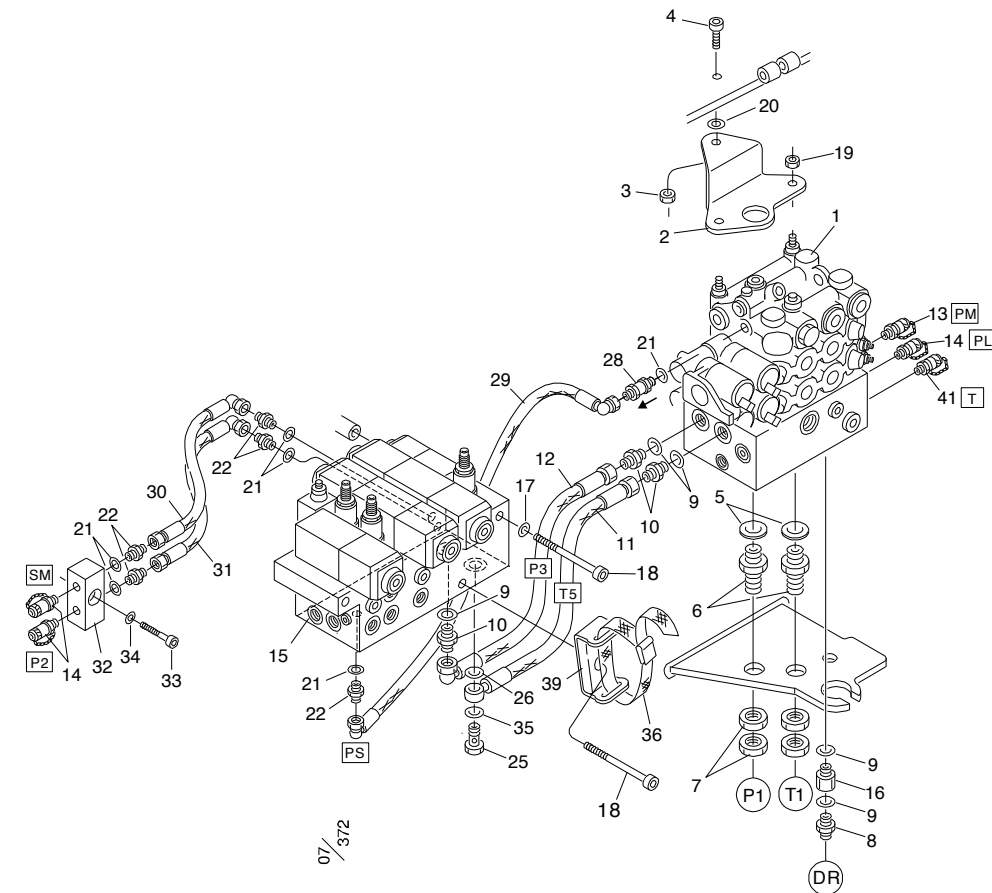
/372	HYDRAULIC SYSTEM / HYDRAULSYSTEM
